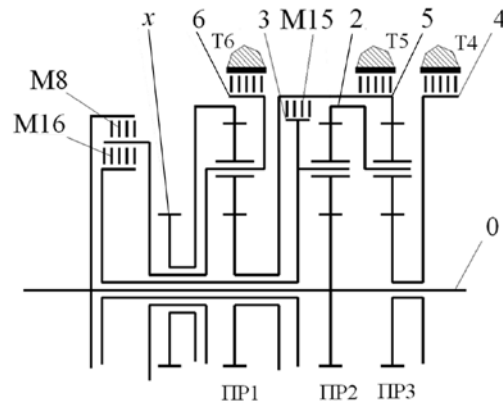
Кинематическая схема исследуемой планетарной коробки передач:
